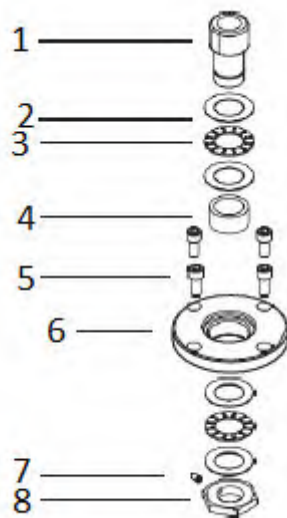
Antriebsmutter-Lagerblock-Baugruppe: Explosionszeichnung
